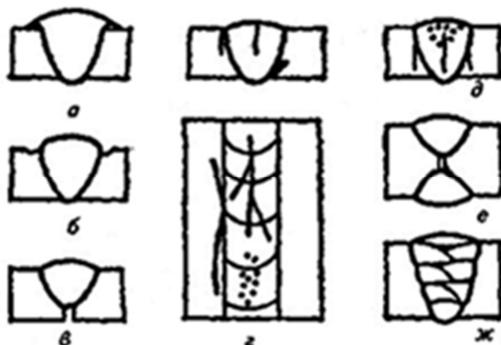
Виды дефектов в сварных соединениях: а – наплыв; б – подрез; в – непровар; г – наружные трещины и поры; д – внутренние трещины и поры; е – внутренний непровар; ж – шлаковые включения
